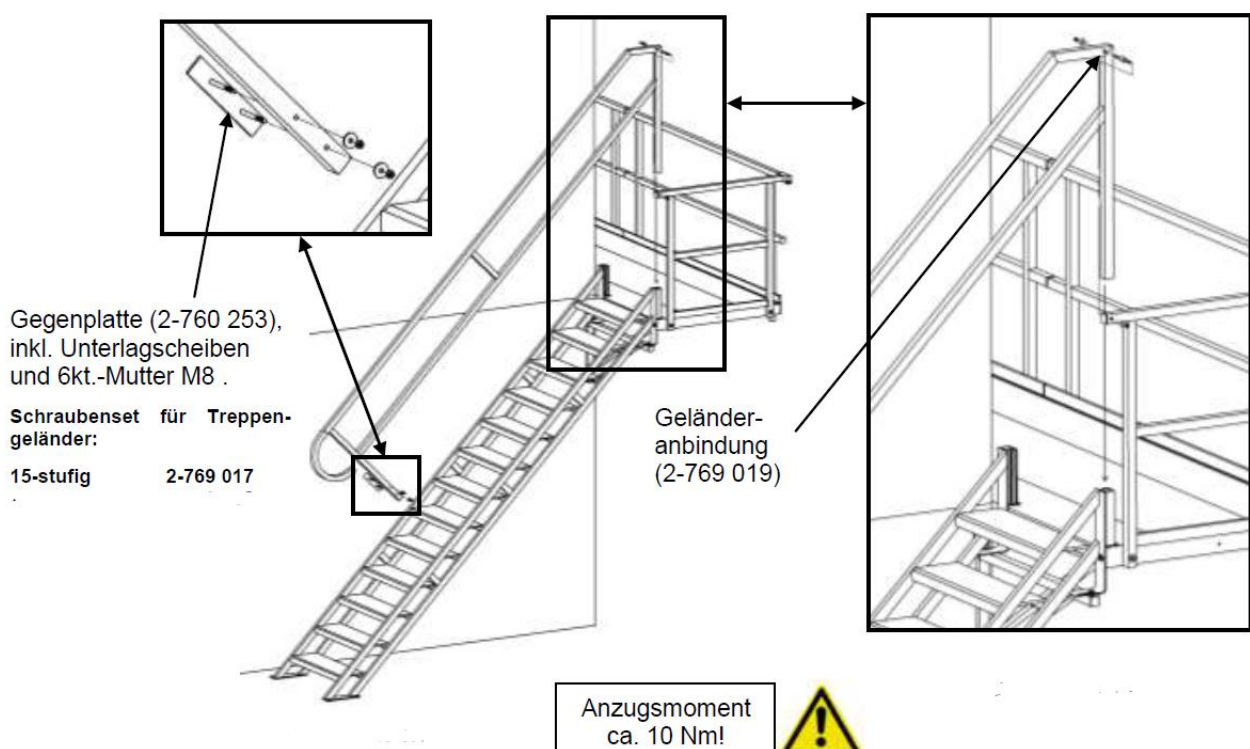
Verbinder für Laufsteg- und Treppengeländer anschrauben
